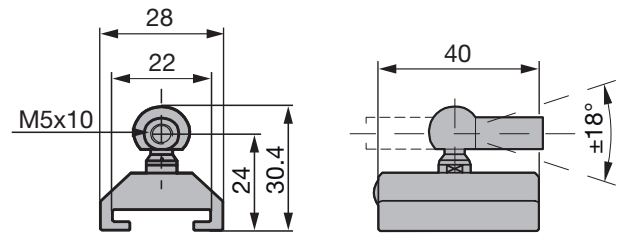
Dimensions de montage du capteur de position BTL5-F-2814-1S
